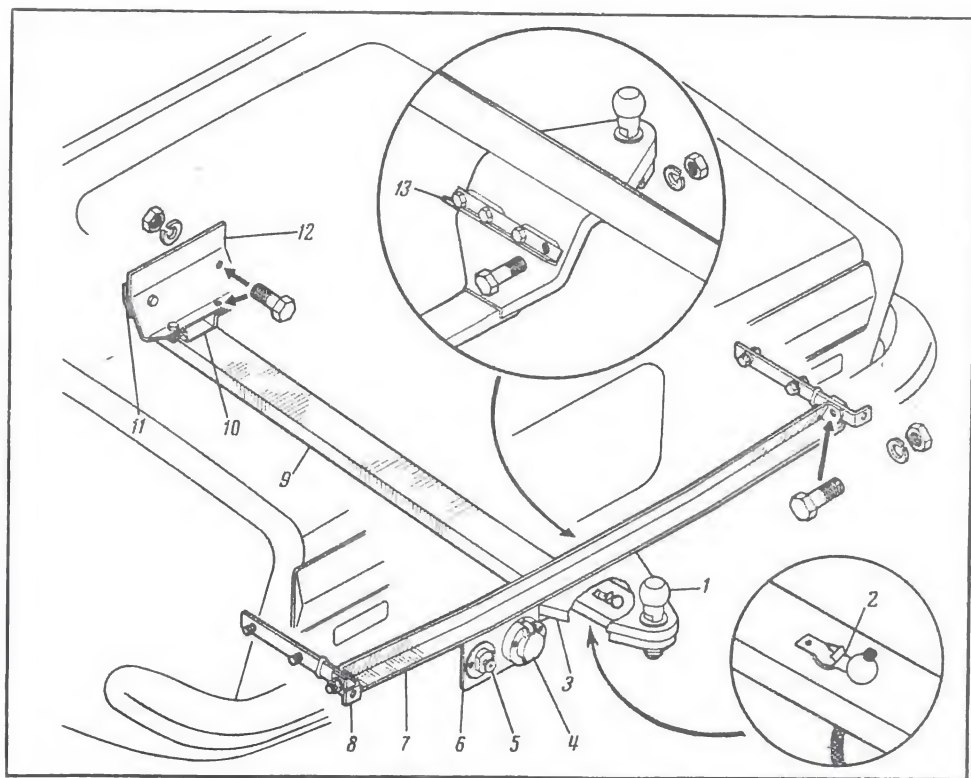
Установка буксирного прибора на ВАЗ—2101: 1 — сцепной шар; 2 — отверстие для страховочного троса; 3 — задний кронштейн балки; 4 — розетка; 5 — выключатель указателей поворота; 6 — кронштейн; 7 — поперечина; 8 — усиленный кронштейн бампера; 9 — балка; 10 — передний кронштейн балки; 11, 12, 13 — накладки.
